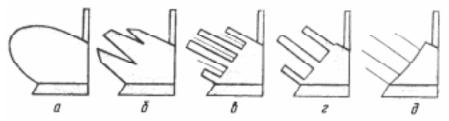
Корпуса с различными рабочими поверхностями: a — традиционный сплошной; δ — щелевой; δ — полосовой с прутками; ε — пластинчатый; δ — прутковый
